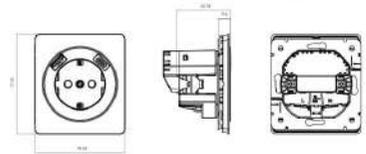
Габаритные и установочные размеры розетки / Figure 2 – Overall and mounting dimensions of socket / 2-сурет – Розетканың габариттік және орнату өлшемдері
